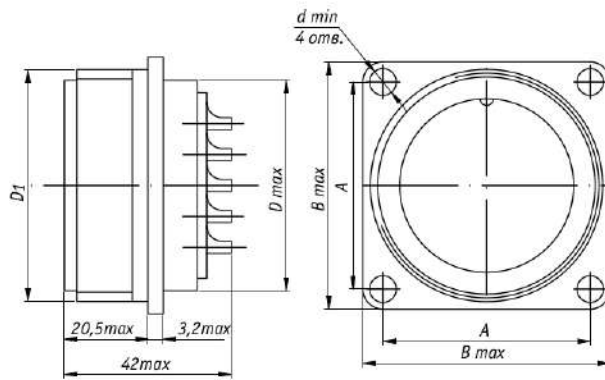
Вилки и розетки типов ШР и СШР приборные без патрубком
